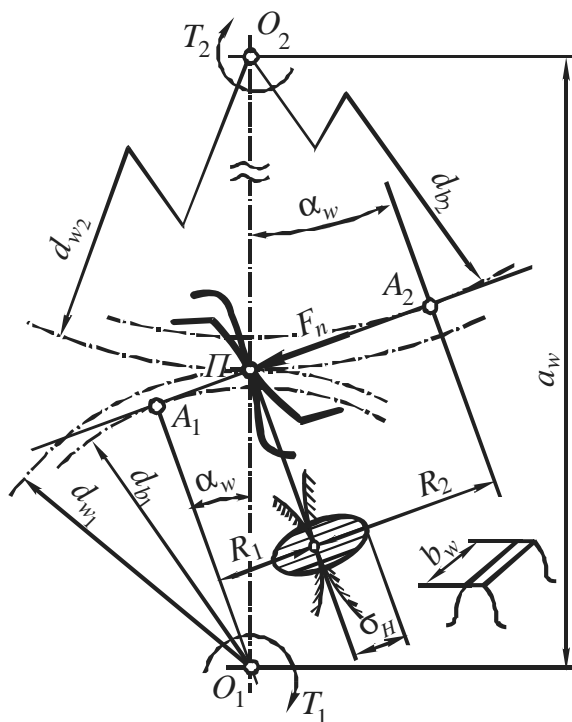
Схема зацепления цилиндрической передачи. Индексы 1 и 2 – относятся к обозначению шестерни и колеса соответственно; d_w – начальный диаметр зубчатого колеса; d – делительный диаметр зубчатого колеса; d_b – диаметр основной окружности зубчатого колеса; α_w – угол зацепления; b_w – ширина зубчатого венца R_1 и R_2 – радиусы кривизны эвольвентной поверхности зуба в полюсе зацепления; P – полюс зацепления; A_1A_2 – линия зацепления; F_n – нормальная сила в зацеплении; T – крутящий момент
